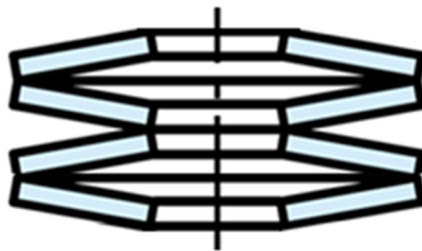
Prinzipbild einer Federsäule, bestehend aus vier wechselsinnig geschichteten Tellerfedern.
